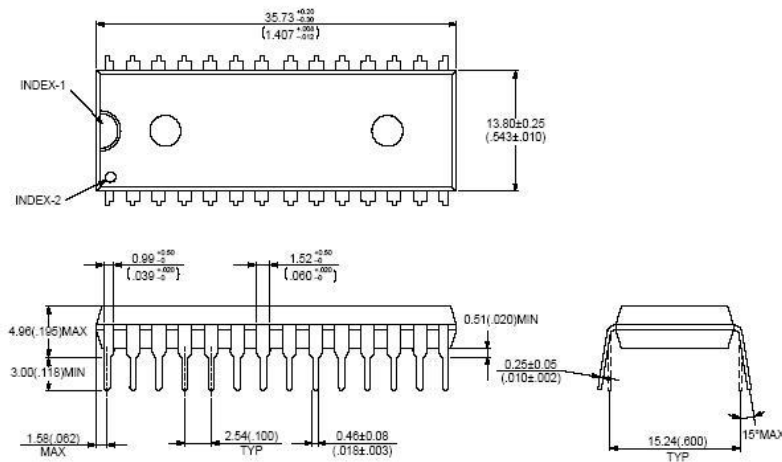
Габаритні розміри мікросхеми АТmega8L-8PU
